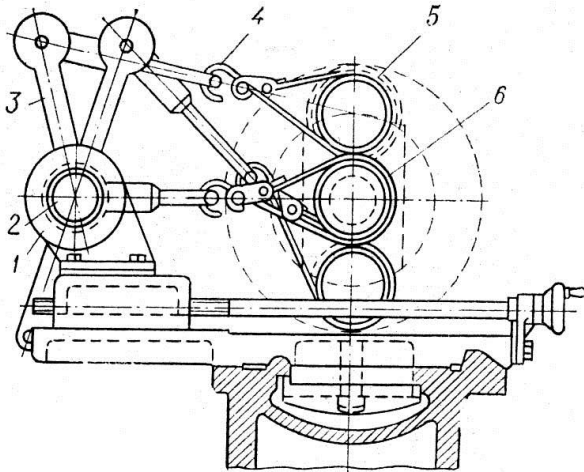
Пристрій до токарного верстата для одночасного полірування шатунних і корінних шийок колінчастого вала:
